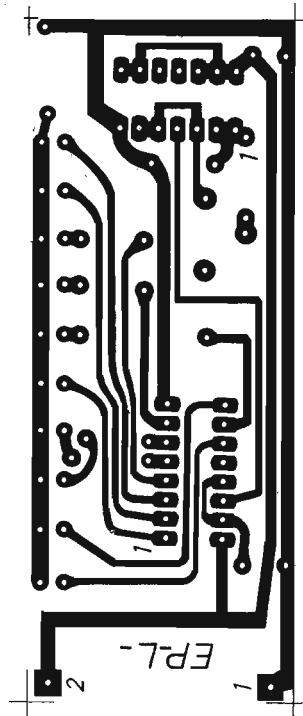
Disegno in grandezza reale del circuito stampato da riprodurre su una basetta-supporto di forma rettangolare e di materiale isolante.
